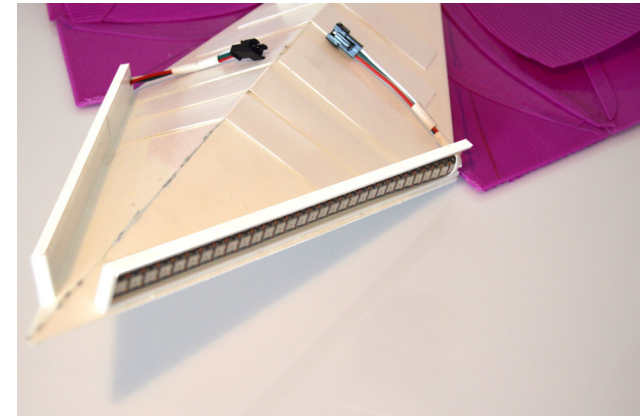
Detalle de refuerzos en las piezas flexibles.
